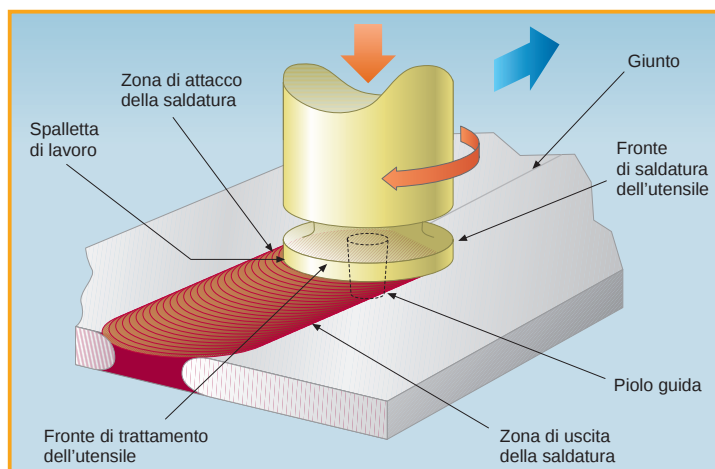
Rappresentazione schematica del processo di Friction stir welding (fonte: TWI).
